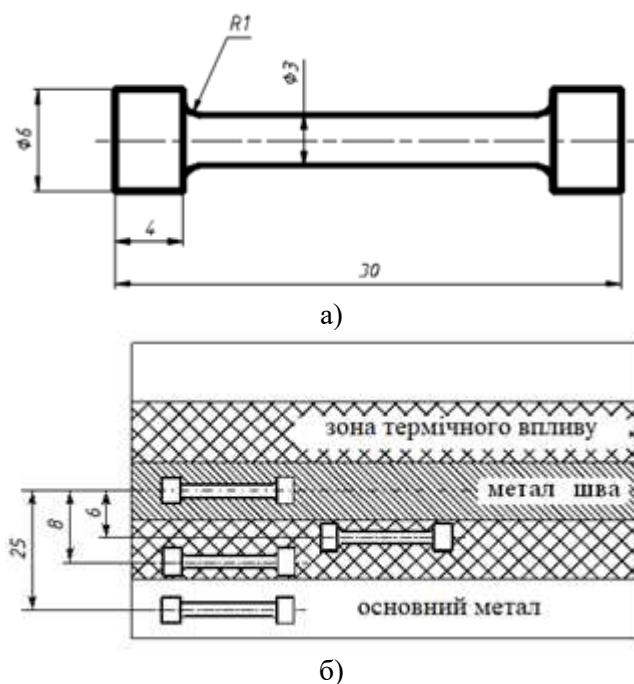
Стандартний циліндричний зразок і схема вирізки
